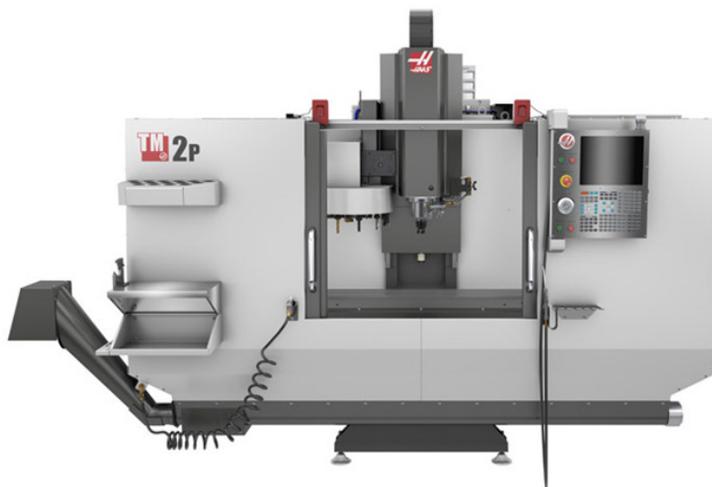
Вертикально-фрезерный станок Haas TM-2P с ЧПУ
